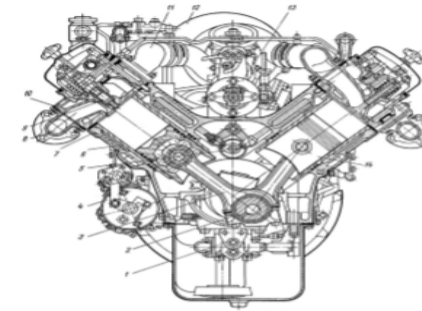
Поперечный разрез двигателя ЯМЗ-238 М2.
